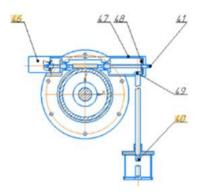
Разрез дросселя с приводом в открытом положении: 44 – держатель магнита; 45 – магнит
